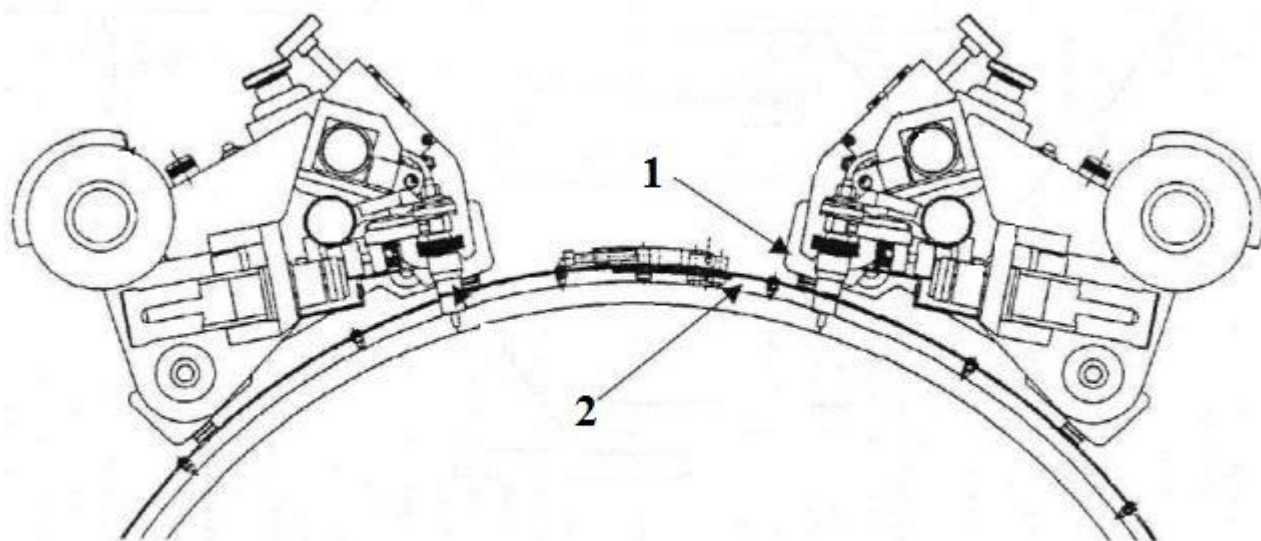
Наружные сварочные головки CRC-EVANS:
